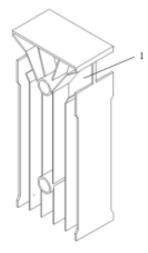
Вертикальный профиль отопительного прибора 1-вертикаьный профиль
